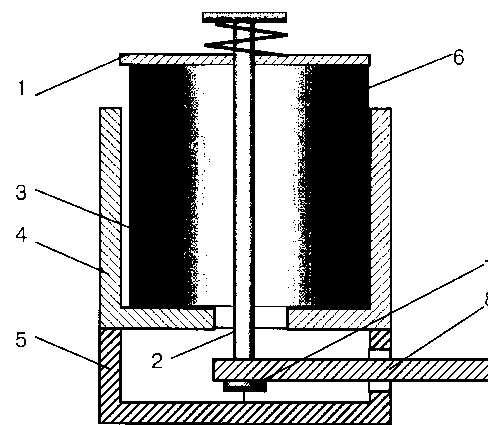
Конструктивная схема резинового виброизолятора подвешенного типа: 1–крышка; 2–стержень; 3–зазор; 4–кожух; 5–корпус; 6–упругий элемент; 7–основание; 8–подшипник.
